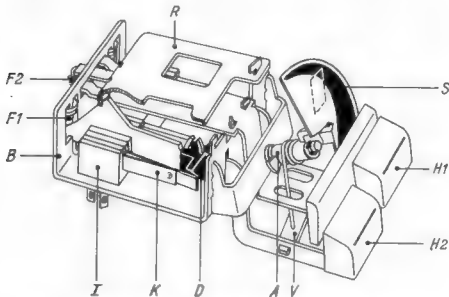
Mechanischer Aufbau der Klangtasten; Bedeutung der Buchstaben im Text
